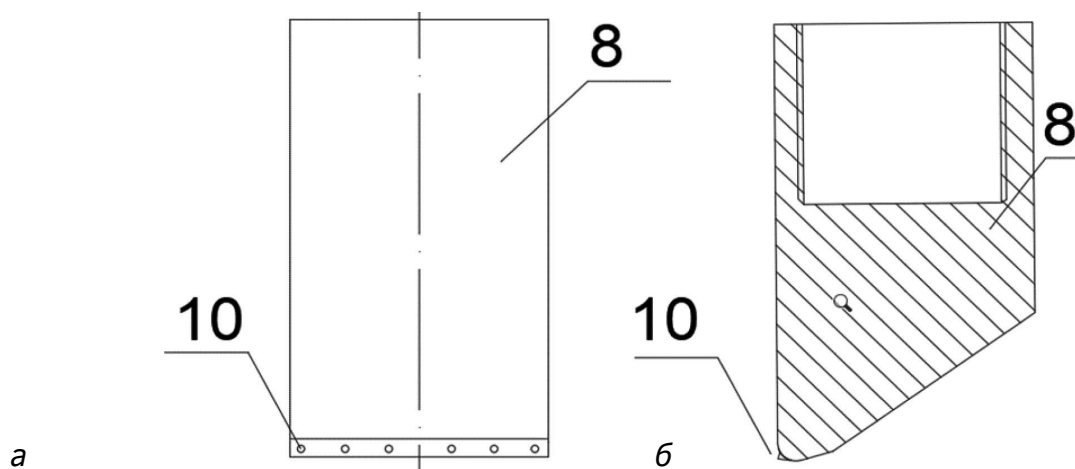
Схема профильного башмака: а — схема размещения резцов на башмаке; б — профиль башмака: 8 — профильный башмак, 10 — породоразрушающий резец
